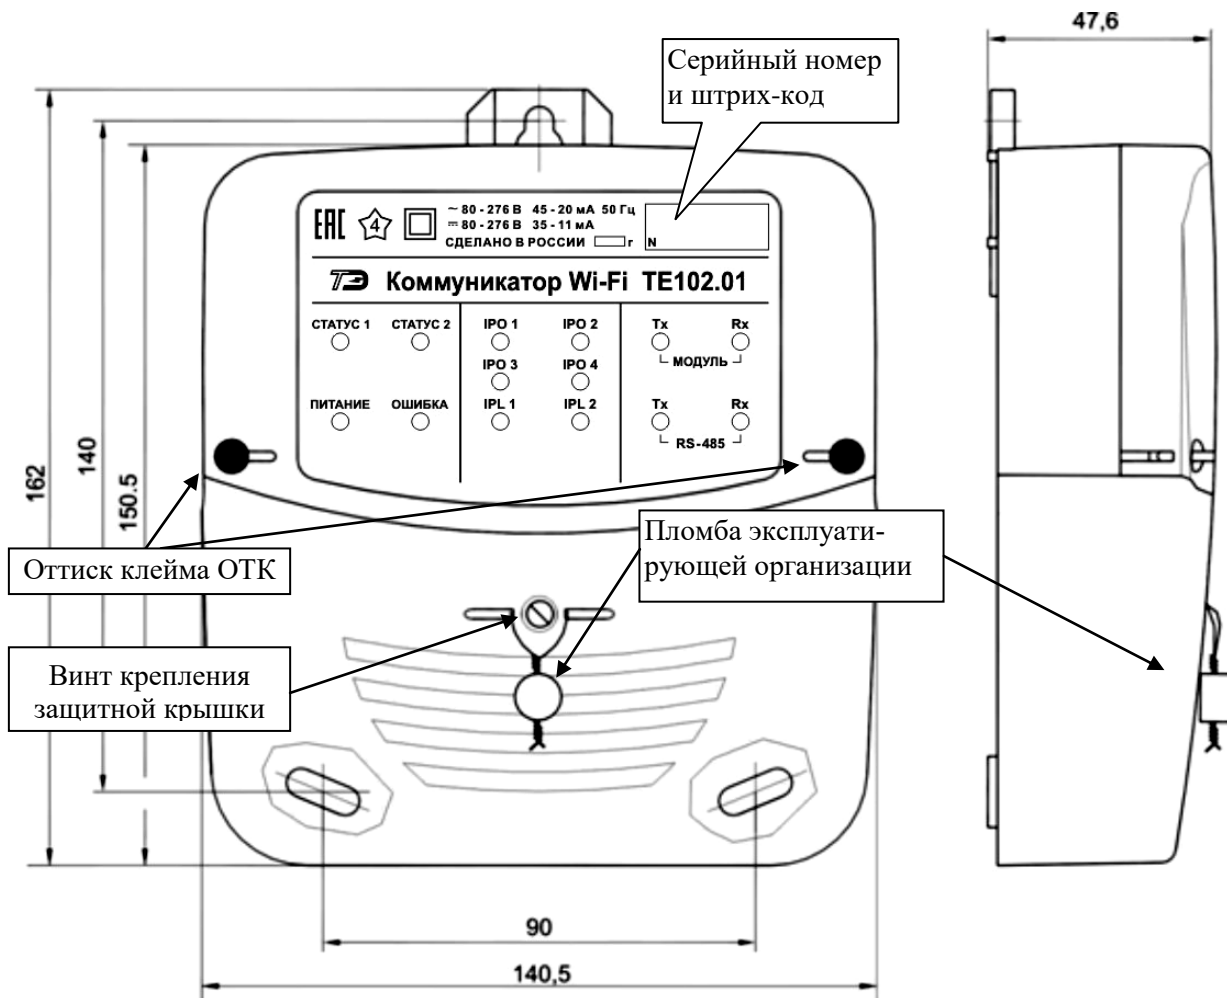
Габаритный чертеж и установочные размеры коммуникатора Wi-Fi TE102.01 с защитной крышкой
